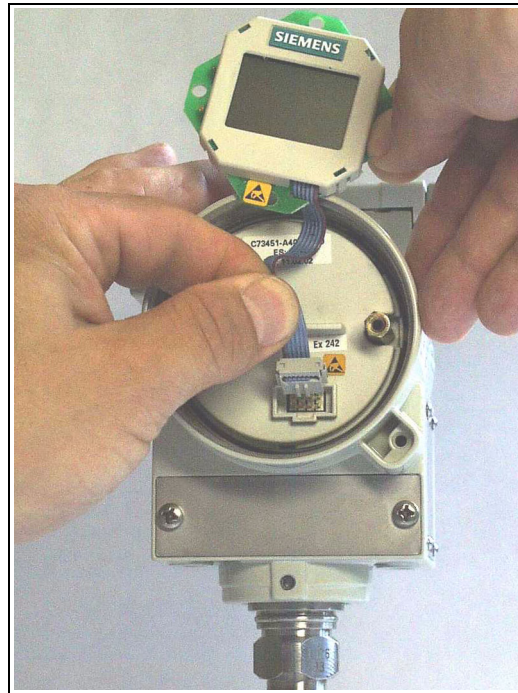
Führungsgerechtes Aufstecken der Anzeige
